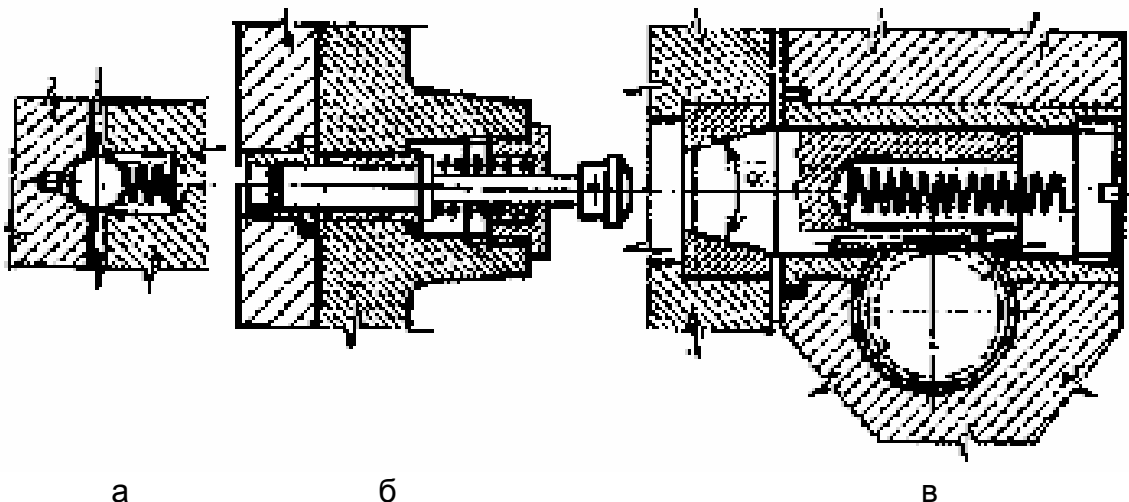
Фіксатори: а – кульковий; б, в – з витяжними циліндричним і конічним пальцями відповідно кнопочного та рейкового типу
